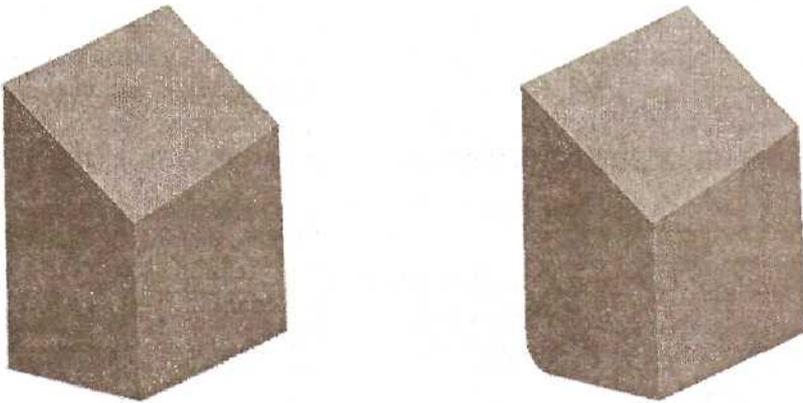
Заготовка верхнего щитка после обрезки поверхностями и скругления нижнего ребра
